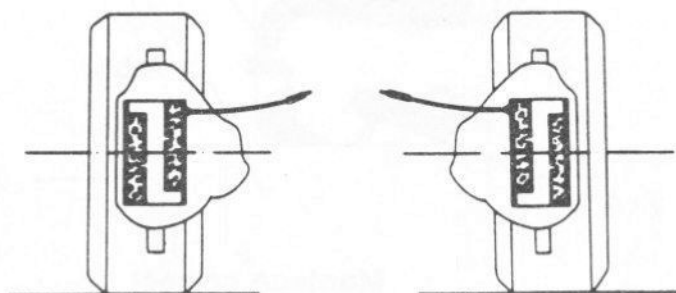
Vue avant des étriers à plaquettes décentrées – étriers de frein à disque Bendix DBA (Sec 17)
